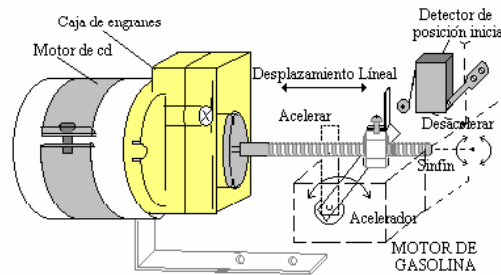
Acoplamiento mecánico del motor al sinfín, y el detector de posición inicial
